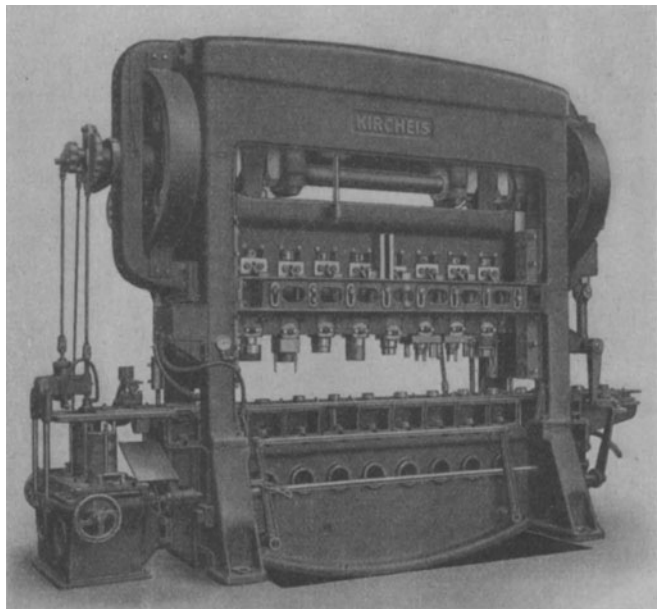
Kurbelpresse mit mehreren nacheinander arbeitenden Werkzeugen: Stufenpresse. Die Zihscheibe bzw. das vorgearbeitete Werkstück wird dem ersten Werkzeug selbsttätig durch Ladescheibe zugeführt und von Werkzeug zu Werkzeug (Stufe zu Stufe) durch Greifer weiterbefördert (KIRCHHEIS).
